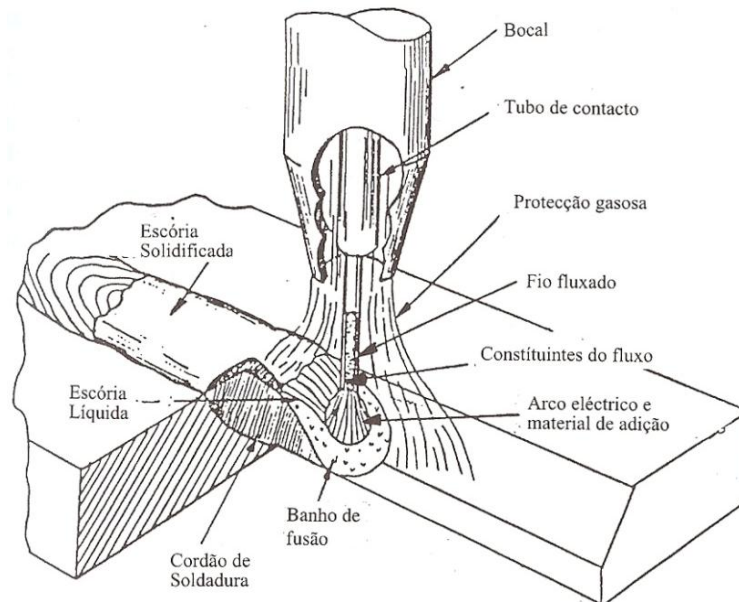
Processo de soldadura por fios fluxados com protecção gasosa [9]
